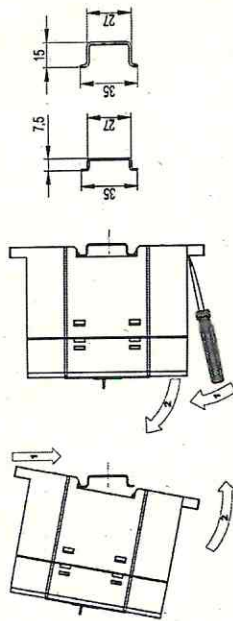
Монтаж прибора с креплением на DIN-рейку
